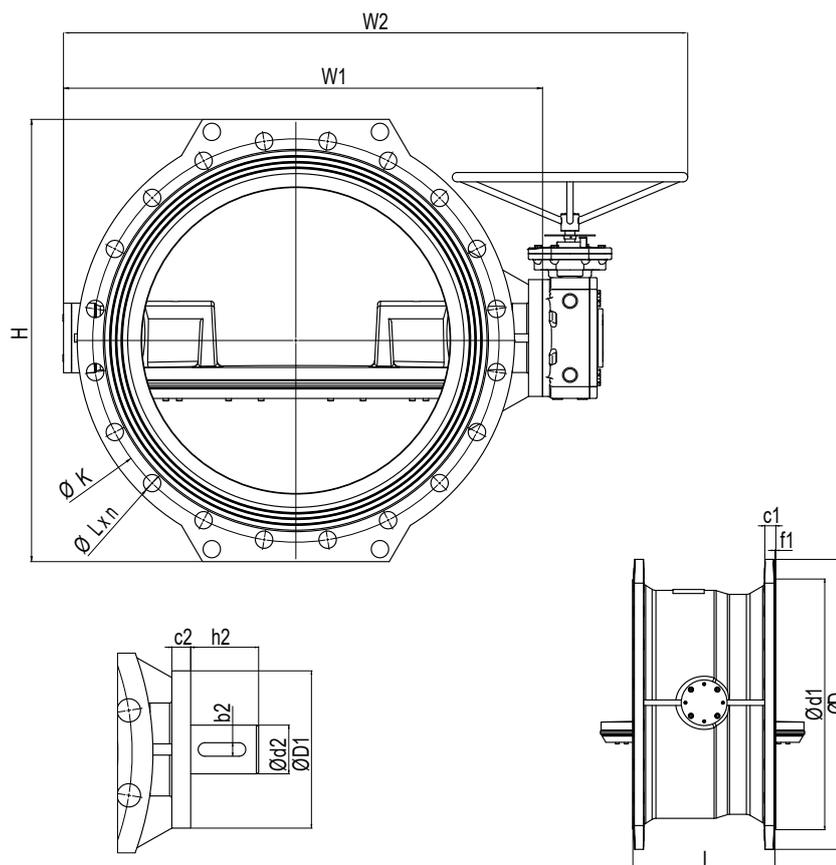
Disegno di sezione PN 25 DN 100 - 700
